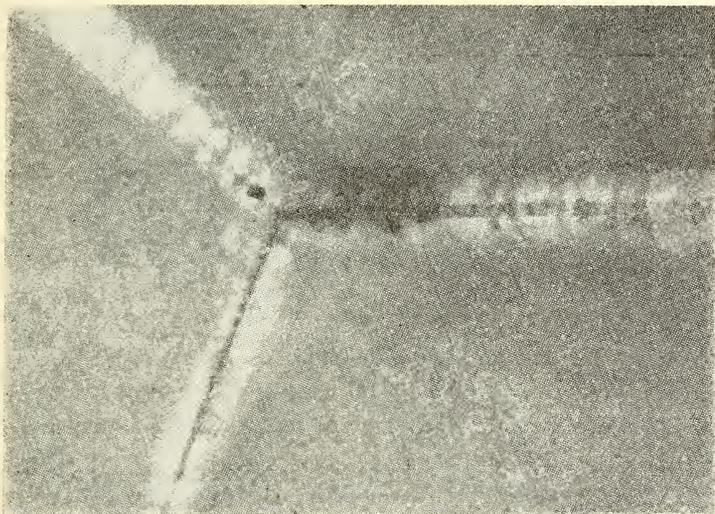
Radiografía de la pieza indicada en la figura 3, mostrando que la soldadura es inaceptable.
